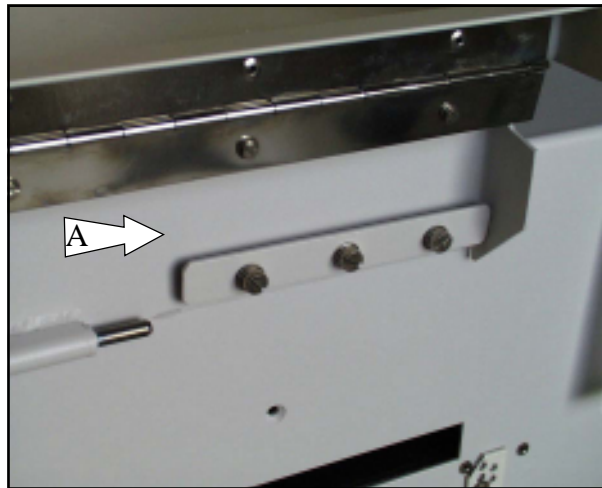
Die Spannplatte, die auf die Aussenseiten des Scharniers montiert ist.
